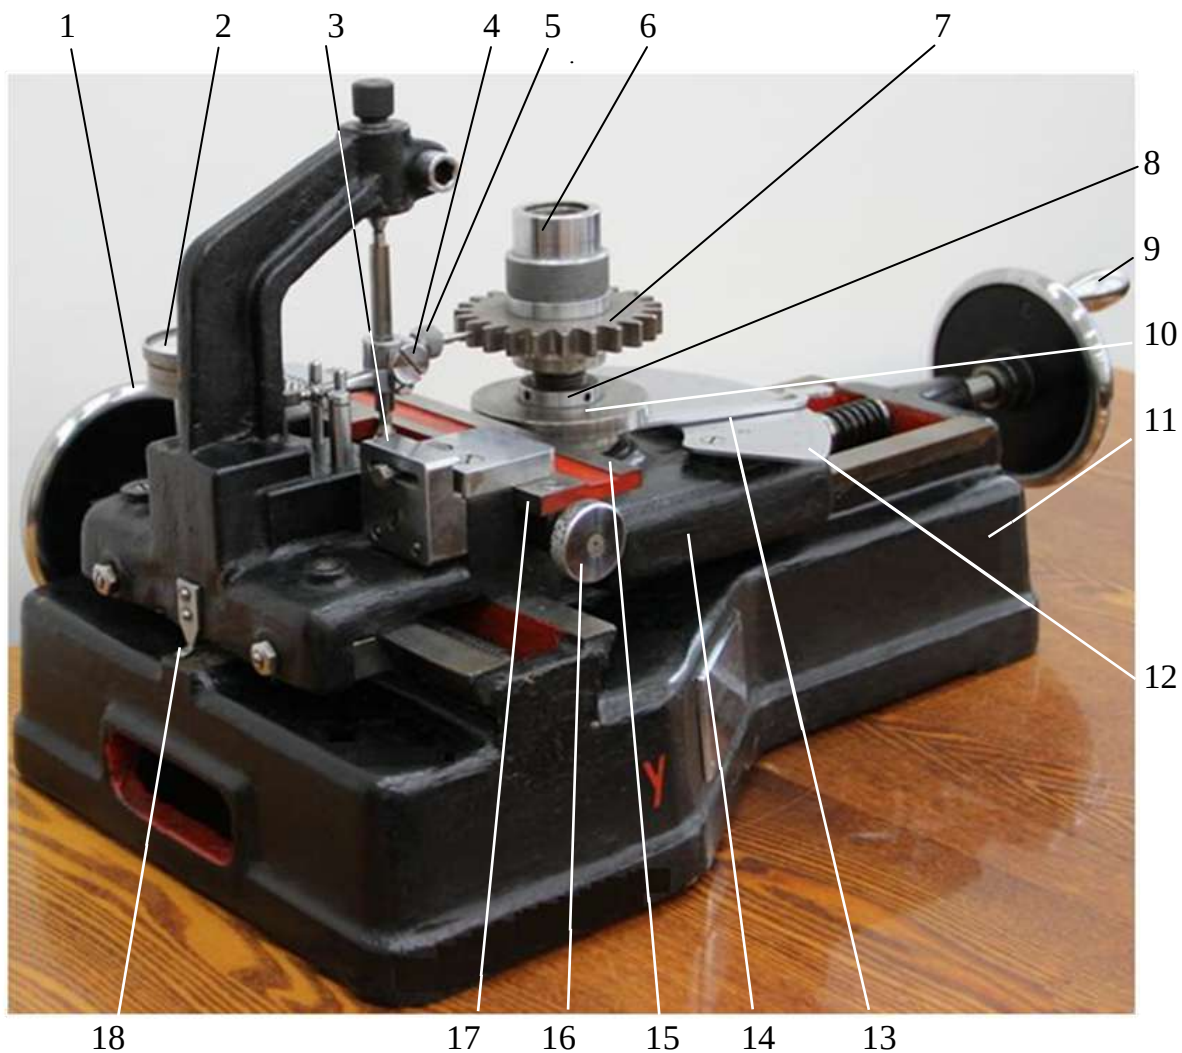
Общий вид индивидуально-дискового эвольвентомера:
